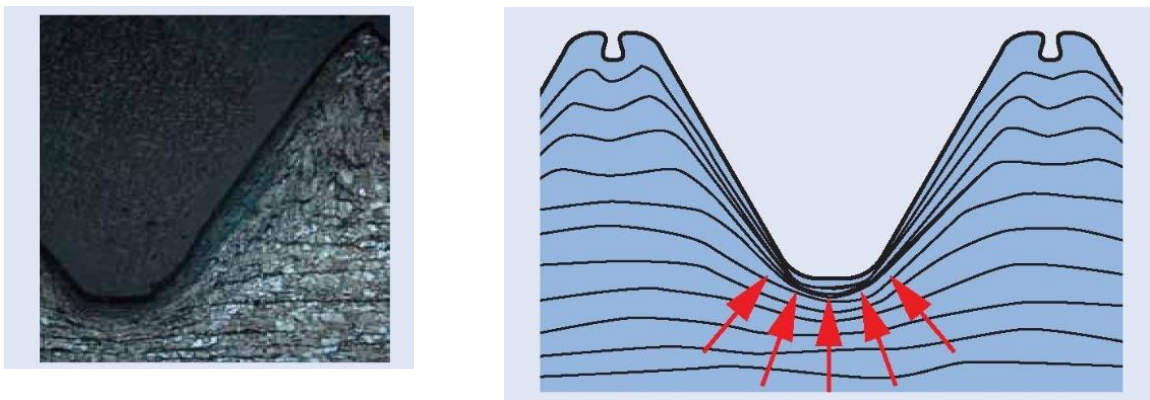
Формування поверхневого шару зміцнених різьбових поверхонь
